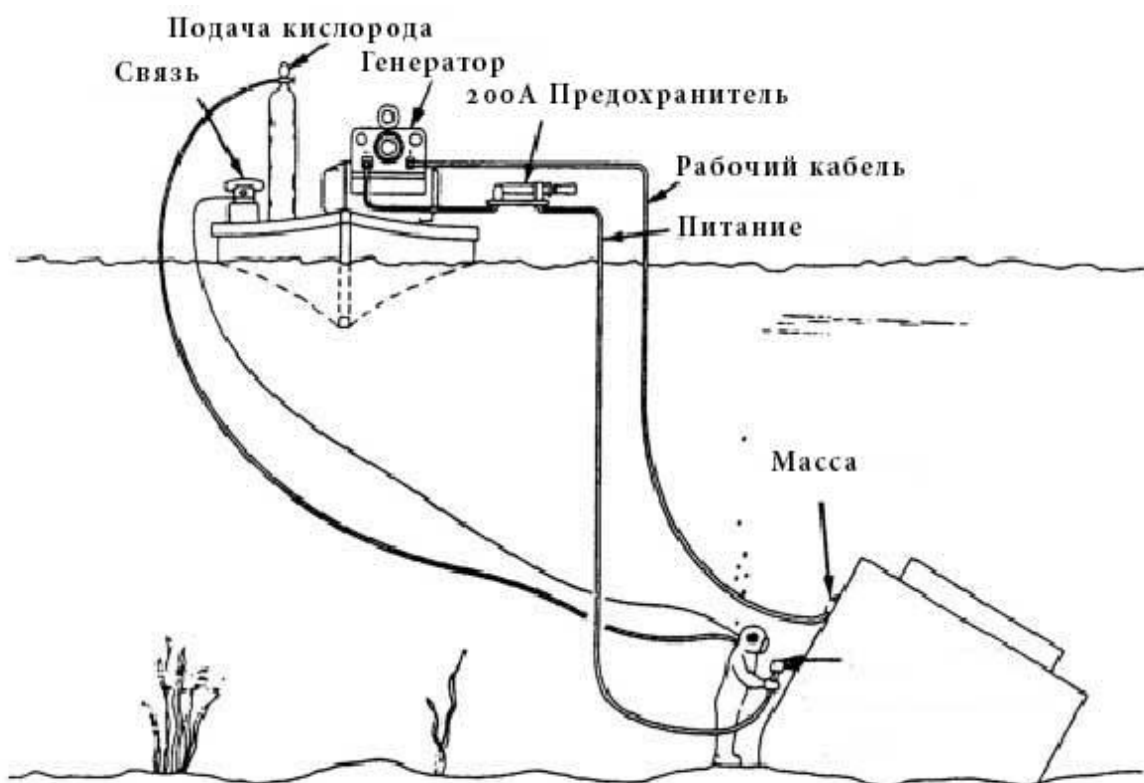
Схема выполнения мокрой подводной сварки
